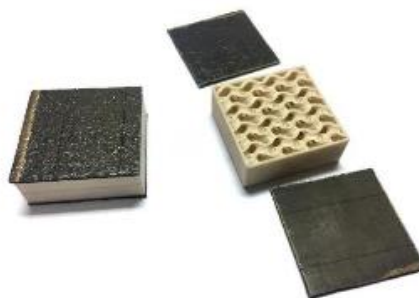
Образец трехслойной конструкции с наполнителем из ЭМ в форме «гироида»
